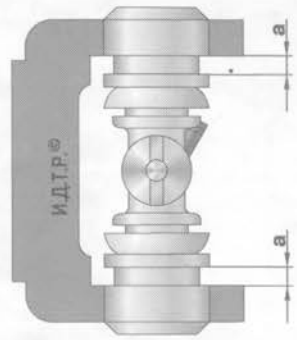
Схема запрессовки подшипников карданного шарнира
